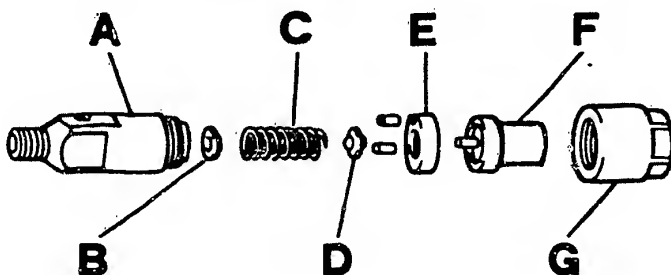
Einzelteile der Einspritzdüsen am 2500 turbo-Dieselmotor: A Düsenhalter - B Einstellscheibe - C Feder - D Druckbolzen - E Zwischenscheibe - F Düse - G Düsenspannhalter.
